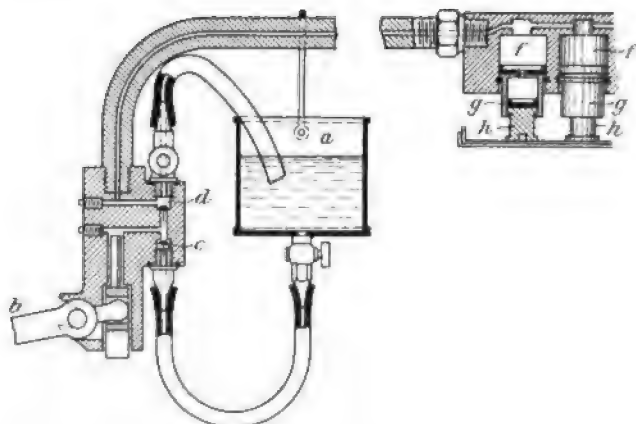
Schnitt durch die Hauptteile der Heckelschen Sprengpumpe.
